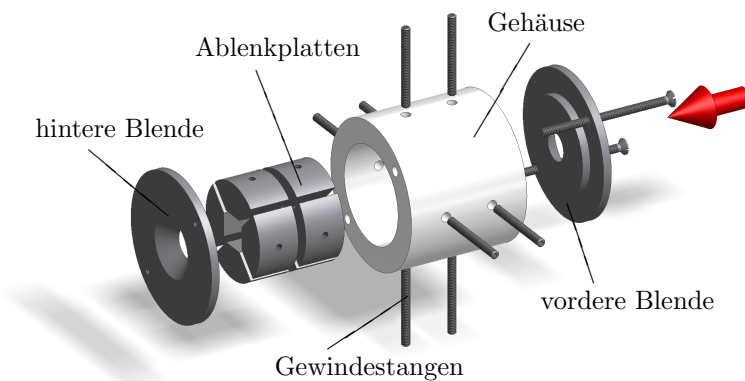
Technische Zeichnung des Einzelablenkers. Die vier Ablenkplatten mit inneren planen Flächen werden durch vier Gewindestangen an das isolierende Gehäuse fixiert und zur elektrischen Kontaktierung verwendet. Die Blende wird mittels drei Schrauben an das Gehäuse montiert. Die Emission ist mit einem roten Pfeil angedeutet.
